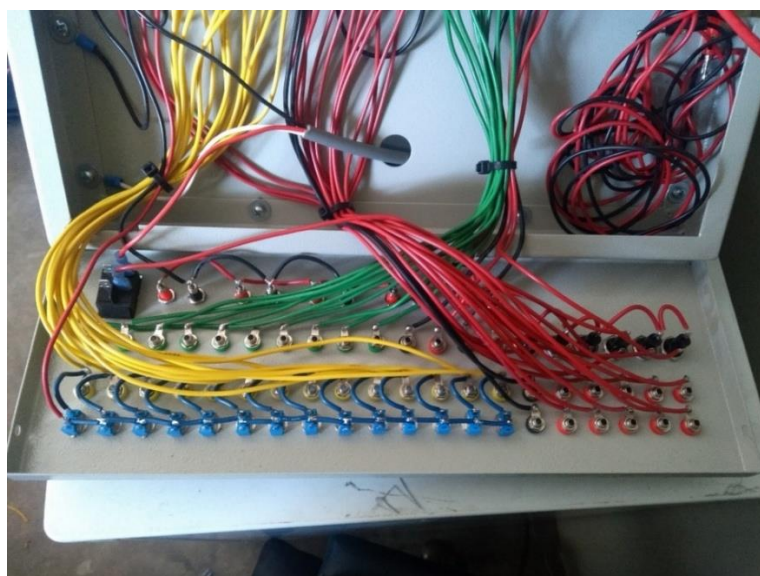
Cableado interno de los módulos con el proceso de soldadura terminado
